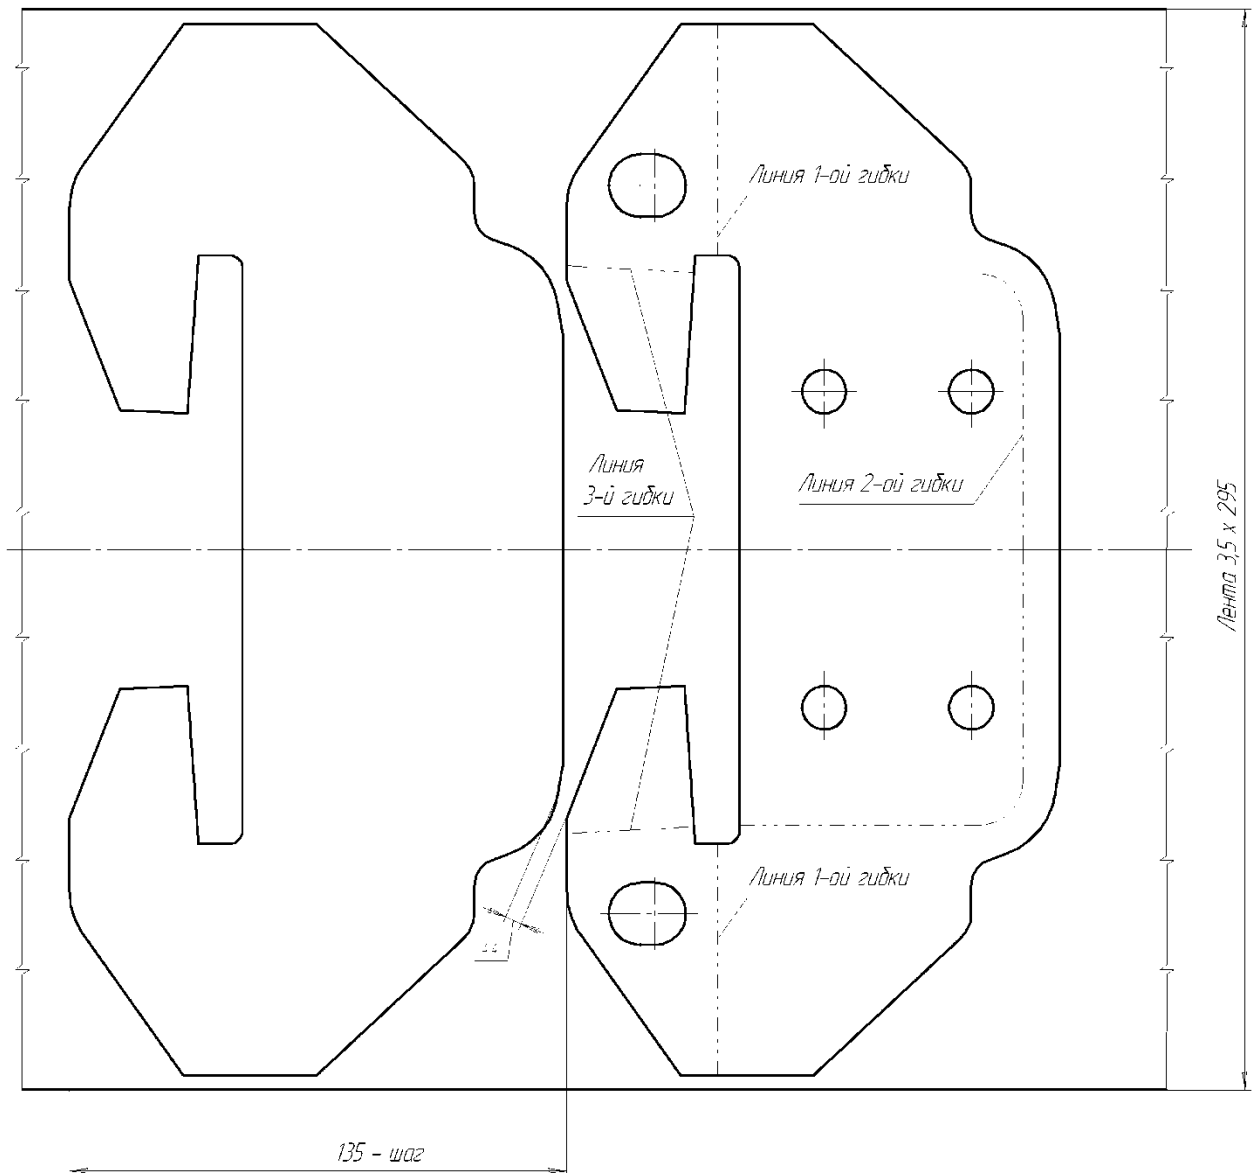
Операция 10.1 – вырубка заготовки и пробивка отверстий
